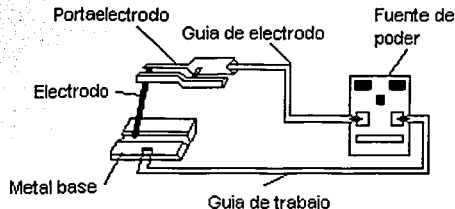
Diagrama del circuito de soldadura para el proceso SMAW [2].
